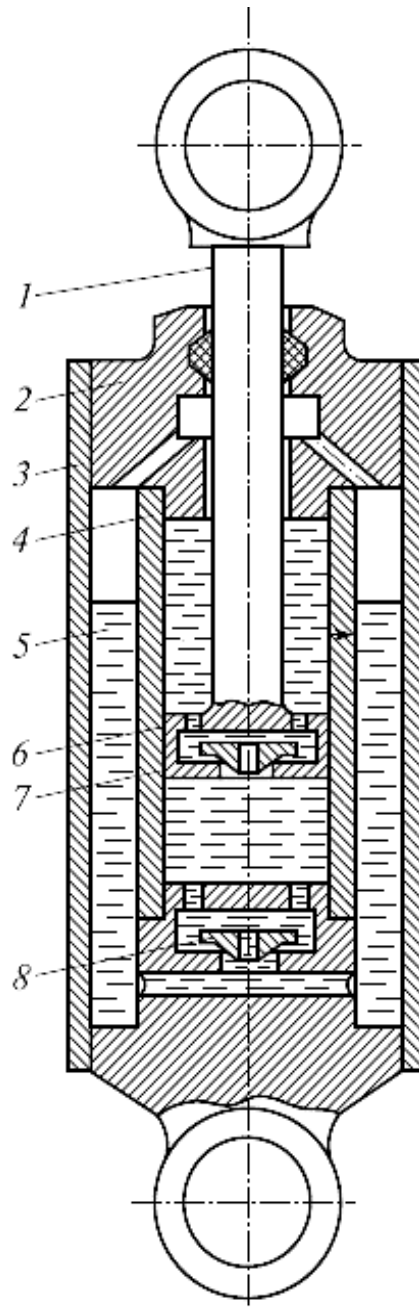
Принципова схема телескопічного пристрою гасителя коливань:
